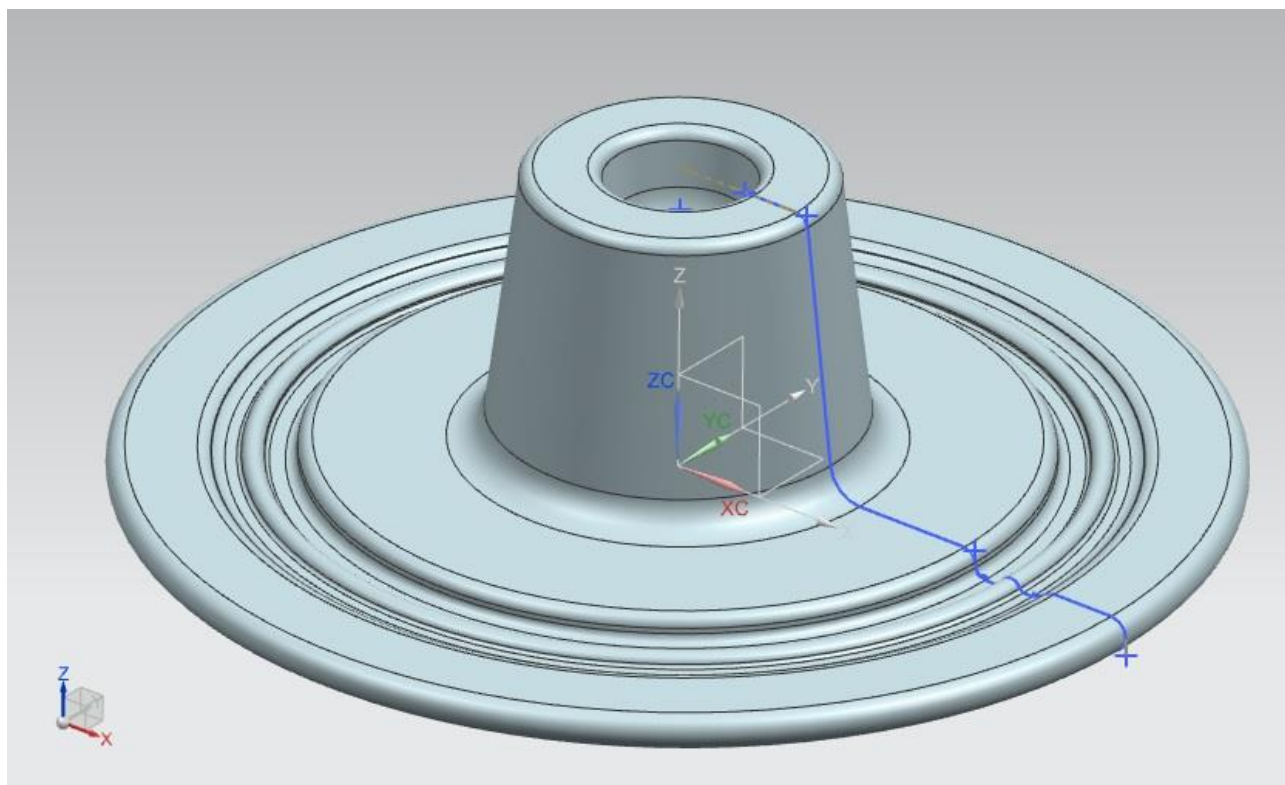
3D-модель гарячої заготовки деталі «Кришка» з додаванням геометрії облойного рівчака V типу
